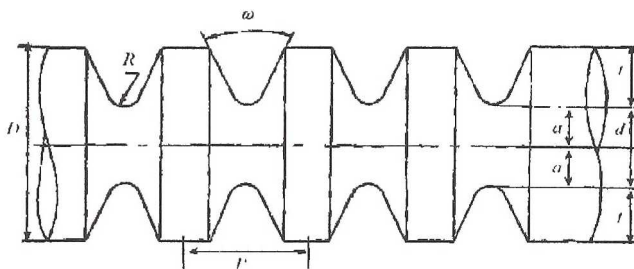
Цилиндрический образец с надрезами V-образного профиля
